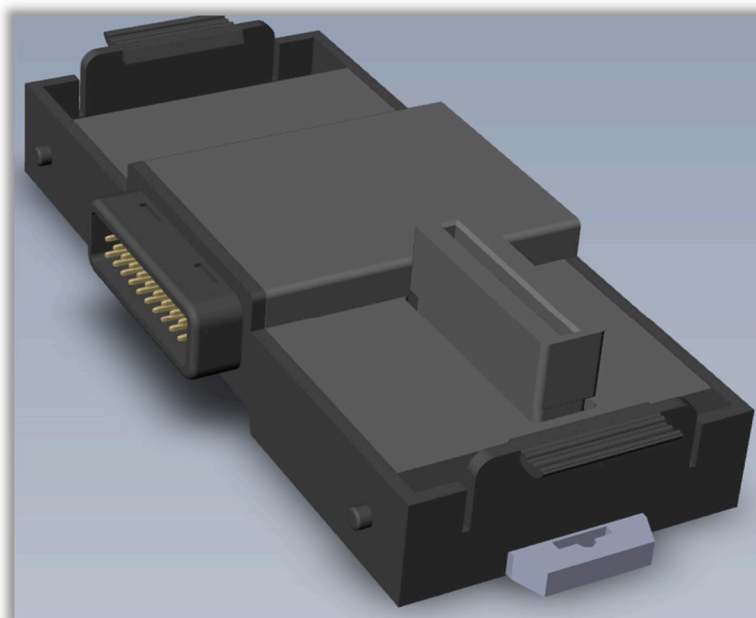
Шинный модуль для модулей ввода-вывода контроллера Simbol-300 S-300-XXXX. Вид слева
